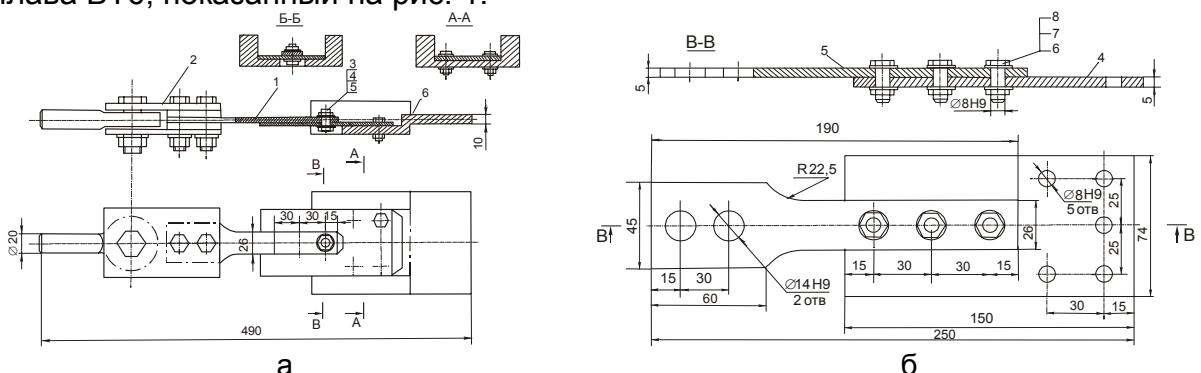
Приспособление и образец для исследования усталостной долговечности односрезных болтовых соединений из сплава ВТ6: а – приспособление; б – исследуемый образец: 1 - образец; 2 - шарнирный захват; 3 - жесткий захват; 4 - пластина; 5 - испытуемый элемент; 6 - болт 8 - 26 - к_д - ОСТ 1 31132 - 80; 7 - гайка 8 - к_д - ОСТ 1 33018 - 80; 8 – шайба 1,5 – 8 - 14 – Ан. окс.- ОСТ 1 34509 - 80
